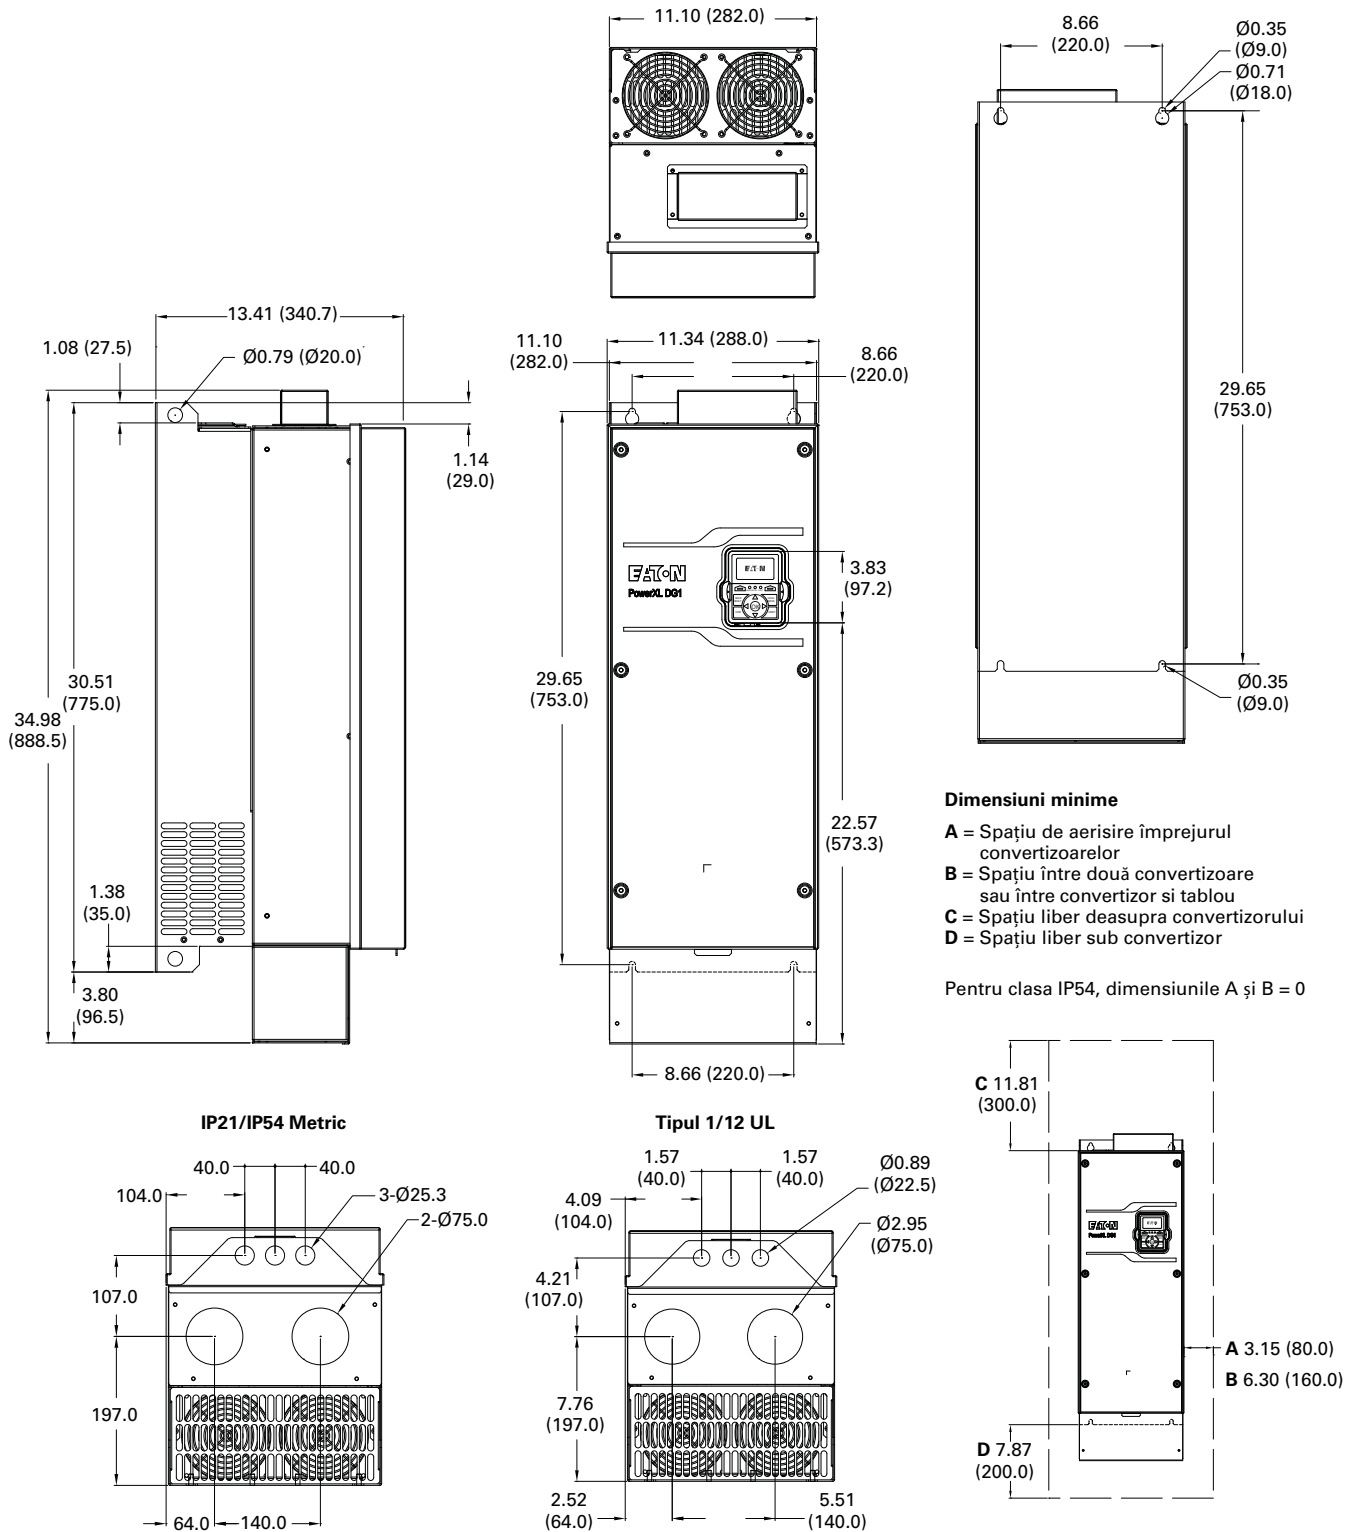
Desen dimensiuni montare pe contrapanou FR4
